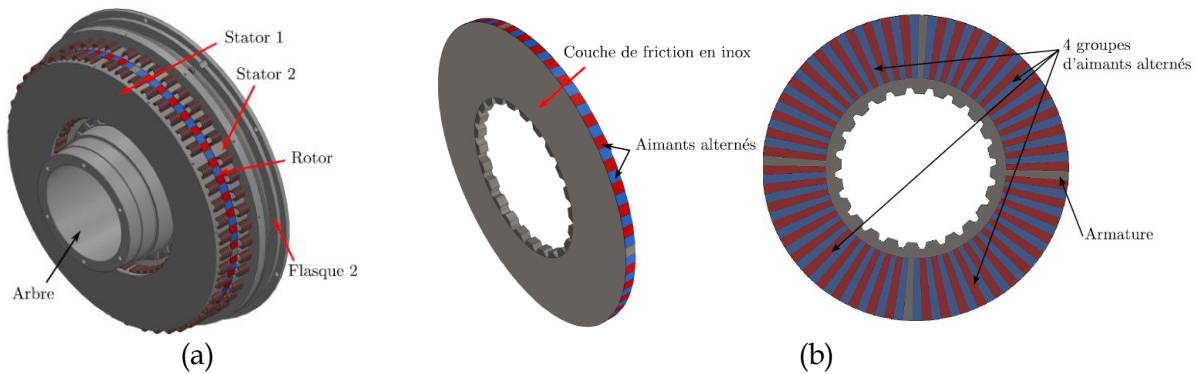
Vues globales : Stator et rotor (a)- Rotor avec et sans couche de friction (b) [32].
